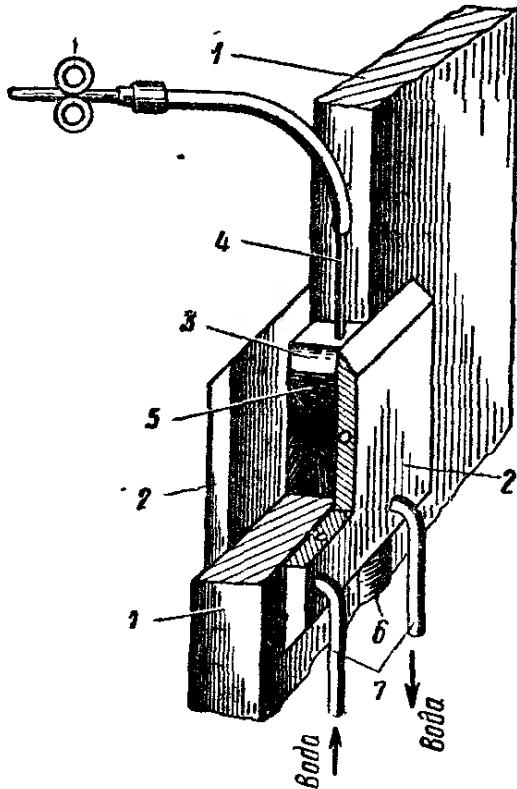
Схема процесса электрошлаковой сварки
